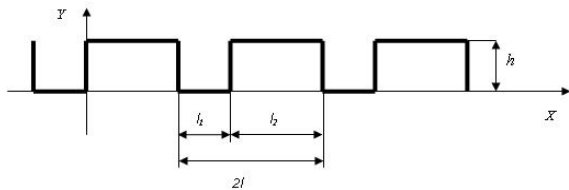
Прямоугольный профиль поверхности эталонной заготовки
